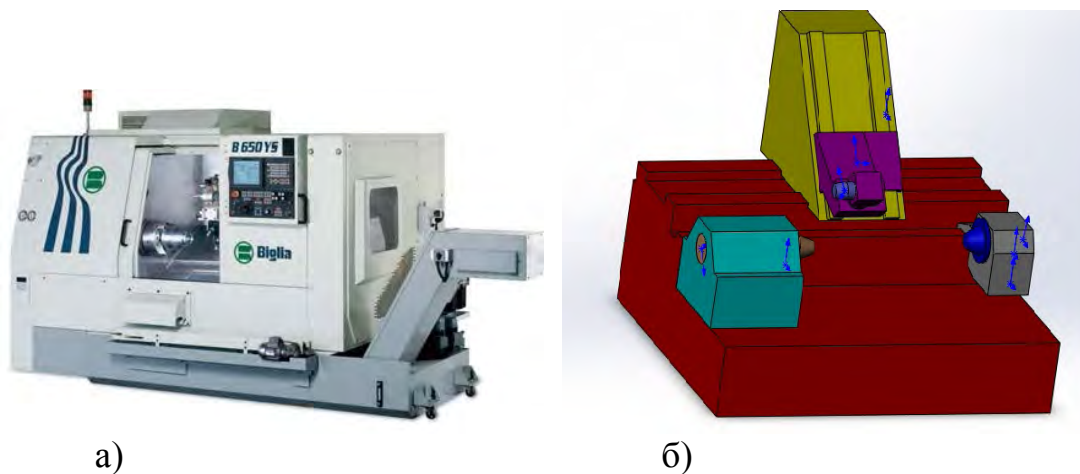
Общий вид и компоновка станка Biglia B545 M
